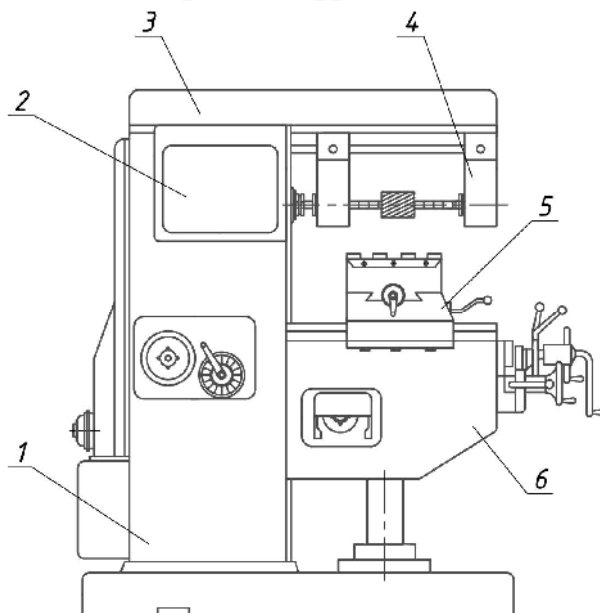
Загальний вигляд горизонтально-фрезерного верстата
